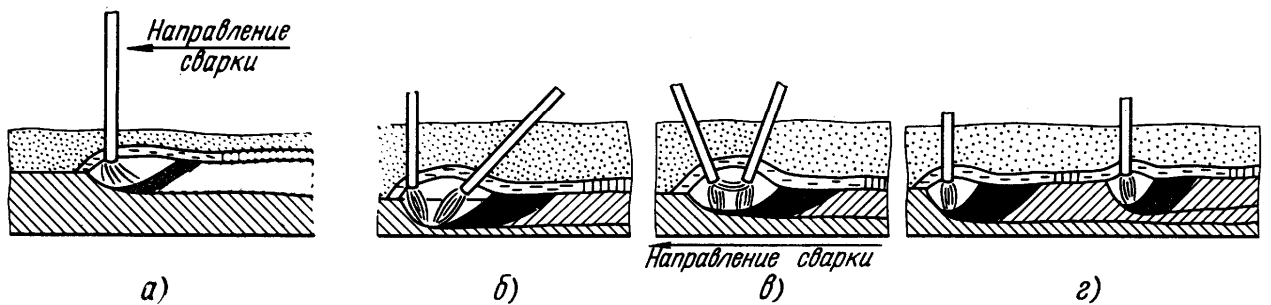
Схемы автоматической дуговой сварки под флюсом: а—одной дугой; б—двумя дугами в общую ванну; в—трехфазной дугой; г—двумя дугами в отдельные ванны
